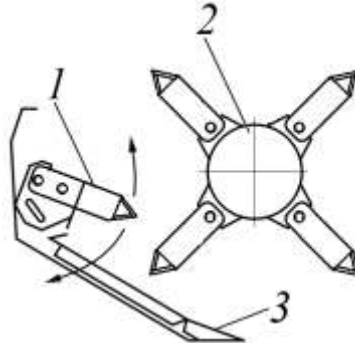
Схема подрібнювача соломи: 1 – брус з поздовжніми протирізальними ножами; 2 – подрібнювальний барабан; 3 – піддон.
